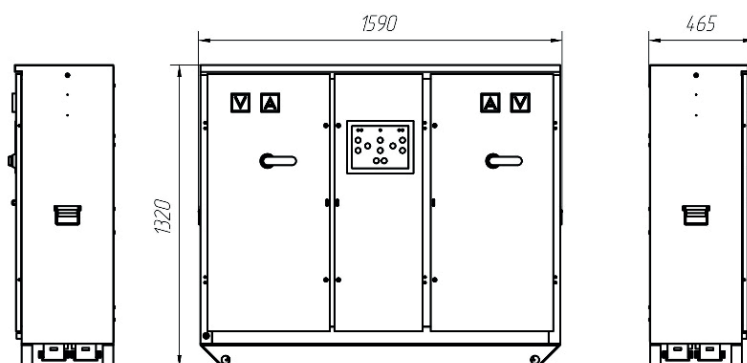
Конструкция шкафа АВР-2х400...2х630А
